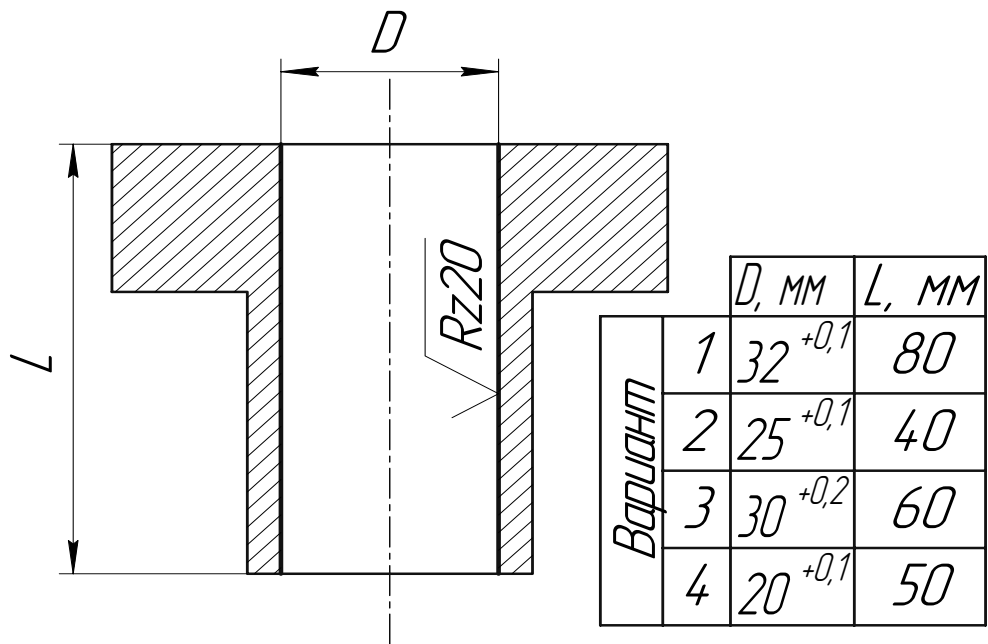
Сверление отверстий сверлами из ВК и ТК
